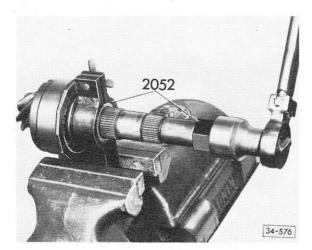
Bague int./roulement à aiguilles: desserrage et serrage
